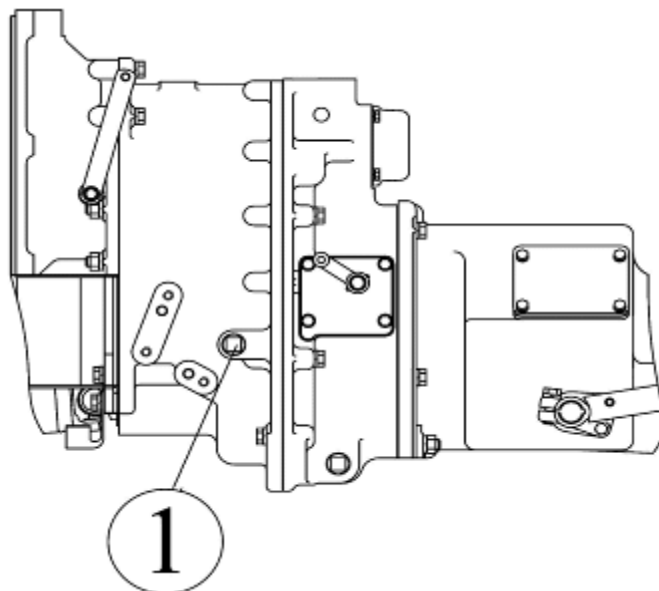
Уровень масла в корпусе коробки передач.
